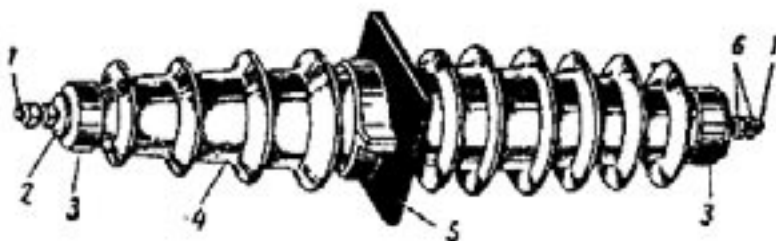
Проходной изолятор для наружной установки ПНБ-35/600
